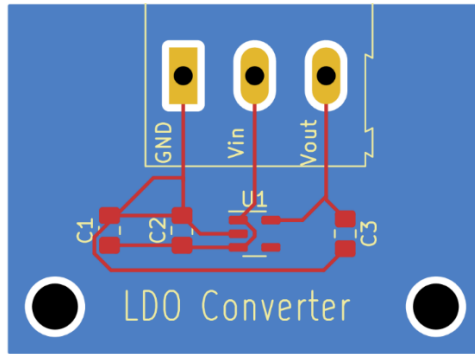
Vista del layout para el PCB del convertidor LDO XC6220, diseñado en KiCad
